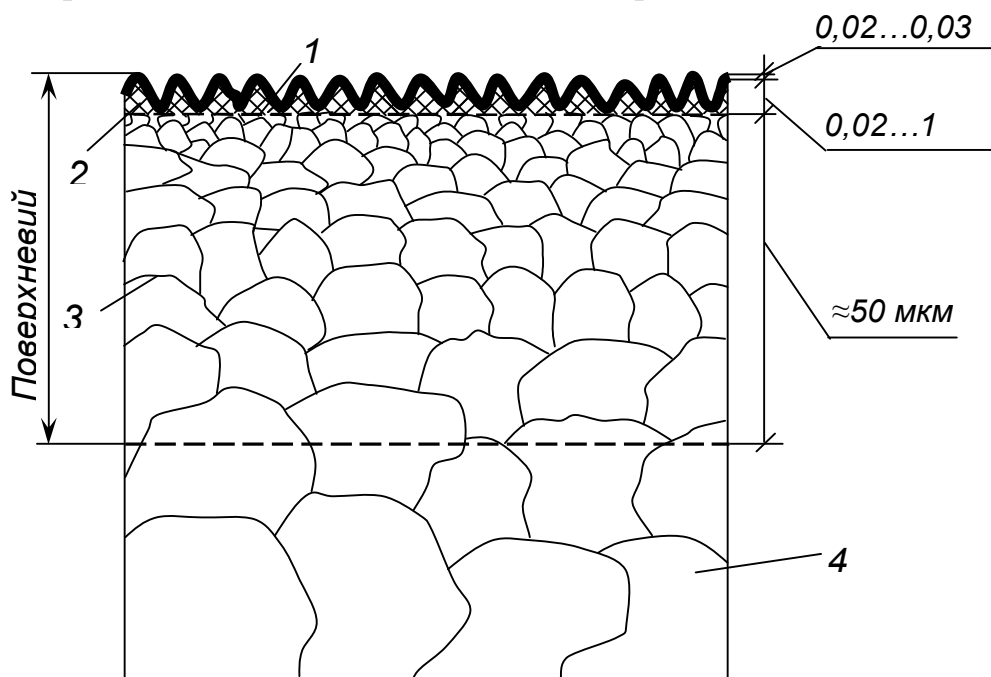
Структура поверхневого шару шліфованої сталеві деталі
